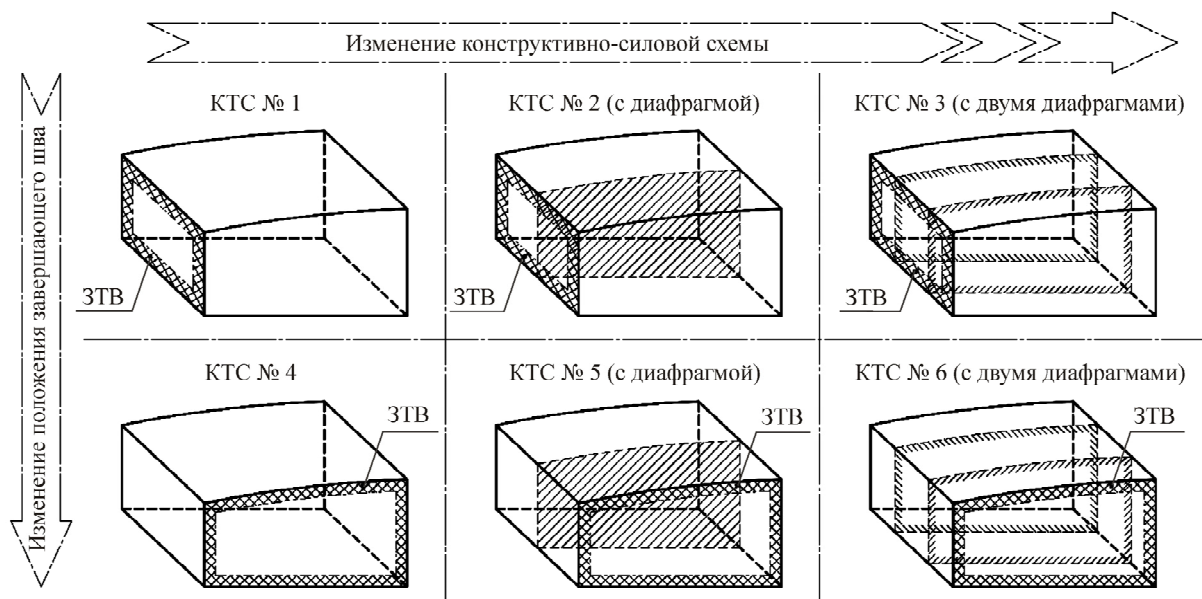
Набор вариантов КТС сварного отсека
